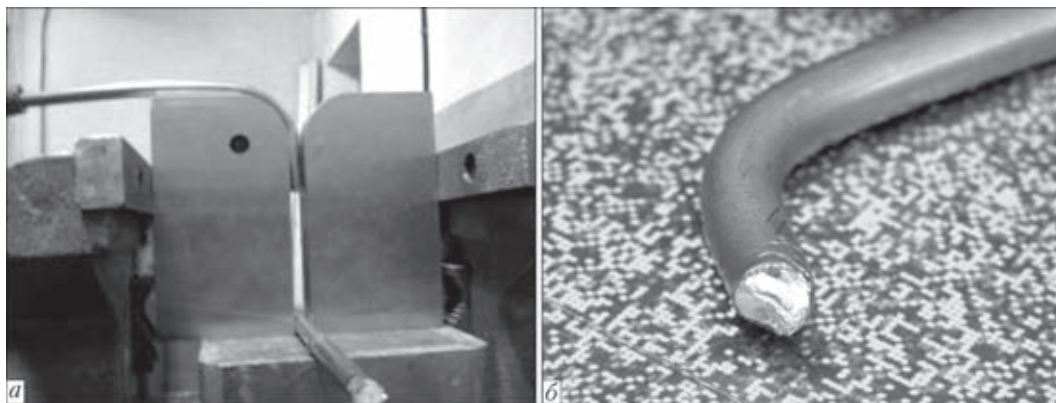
Общий вид способа испытаний на загиб (а) и вид излома прутка (б)
